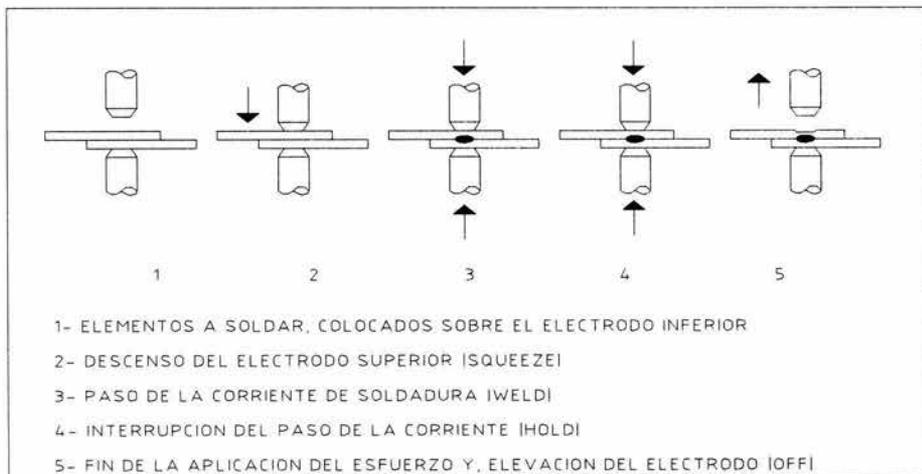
Secuencia básica de soldadura para soldar un par de láminas.
